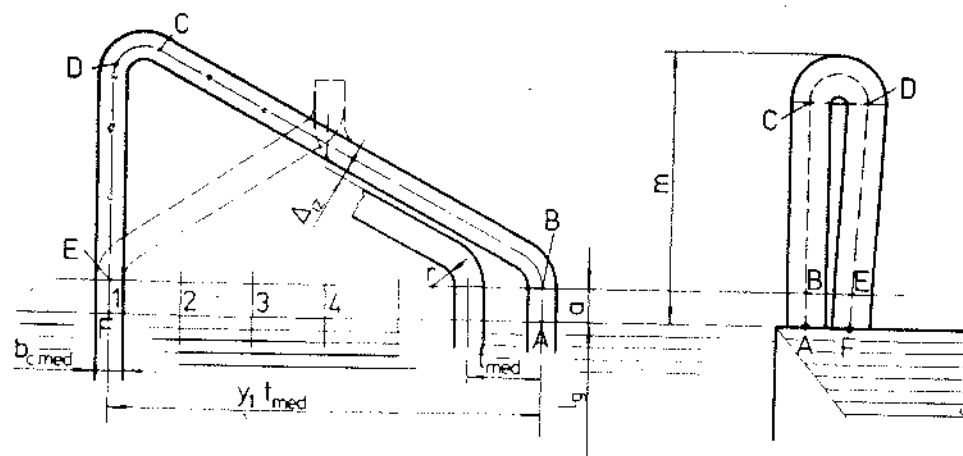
Construcția capătului frontal al bobinelor trapezoidale.
